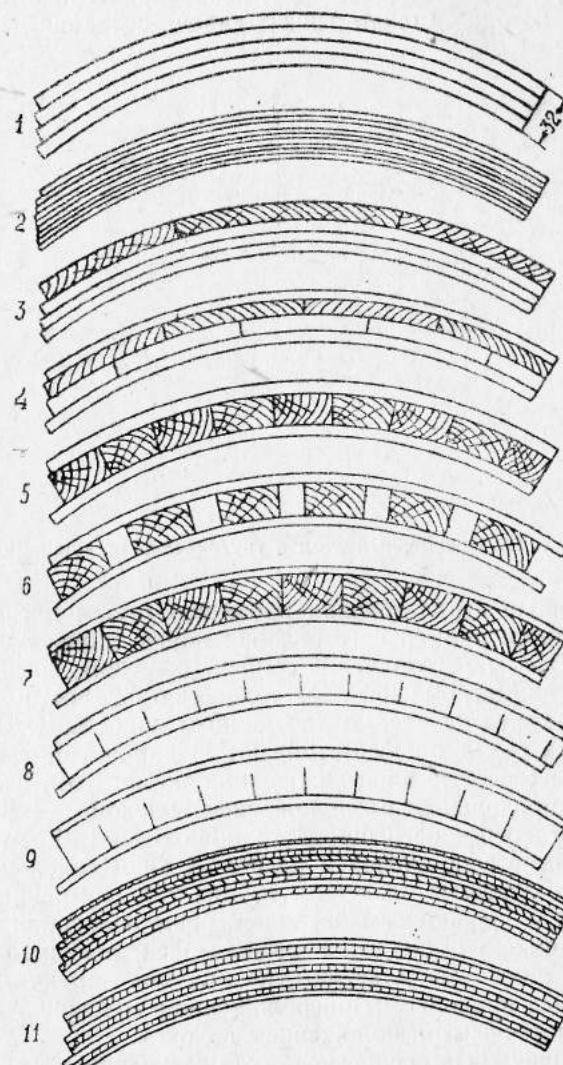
Схема изготовления обвязки крышки круглого стола.
